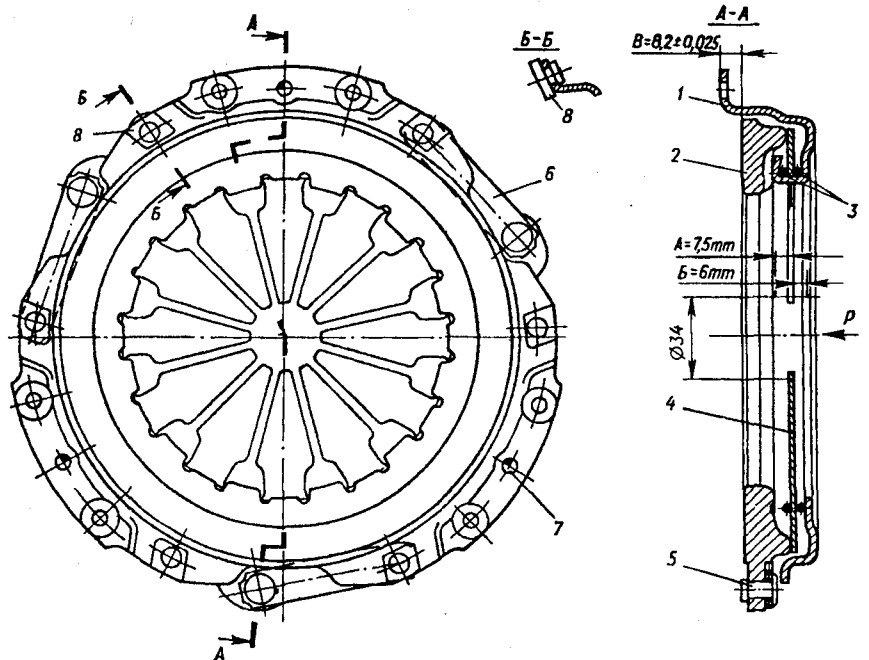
Нажимной диск сцепления: 1 – кожух сцепления; 2 – диск нажимной; 3 – кольца нажимной пружины; 4 – пружина нажимная; 5 – заклепка; 6 – пластина соединительная; 7 – контрольные отверстия; 8 – грузик балансировочный; А=7,5 мм – ход упорного фланца для полного выключения сцепления; Б=6 мм – максимально допустимое перемещение упорного фланца при износе фрикционных накладок; В=(8,2±0,025) мм – толщина кольца, применяемого для контроля механизма сцепления; Р – направление приложения усилия 1000 Н (102 кгс) при ходе выключения 7 мм на $\varnothing 34$ мм
